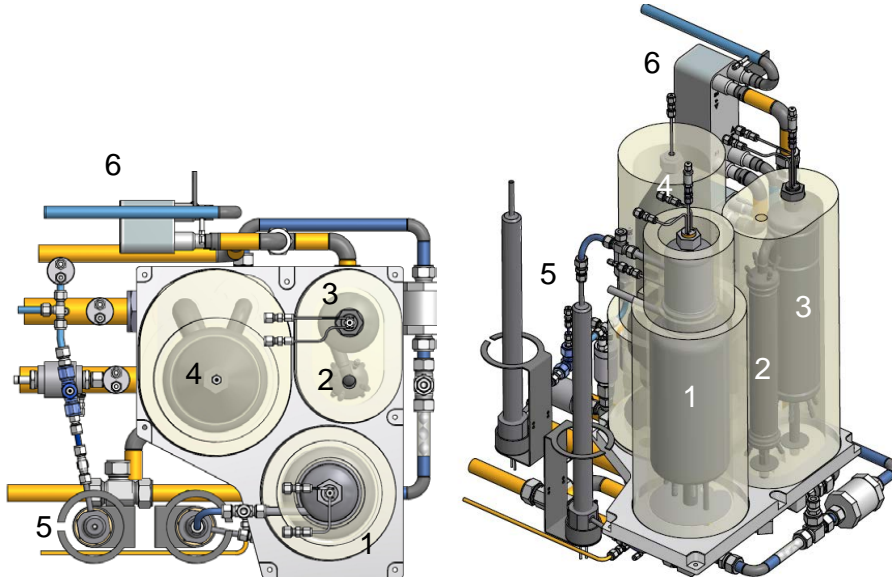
1. Entwurf für das Package Fuel Processing-System, links Draufsicht, rechts: Seitenansicht der Isometrie
